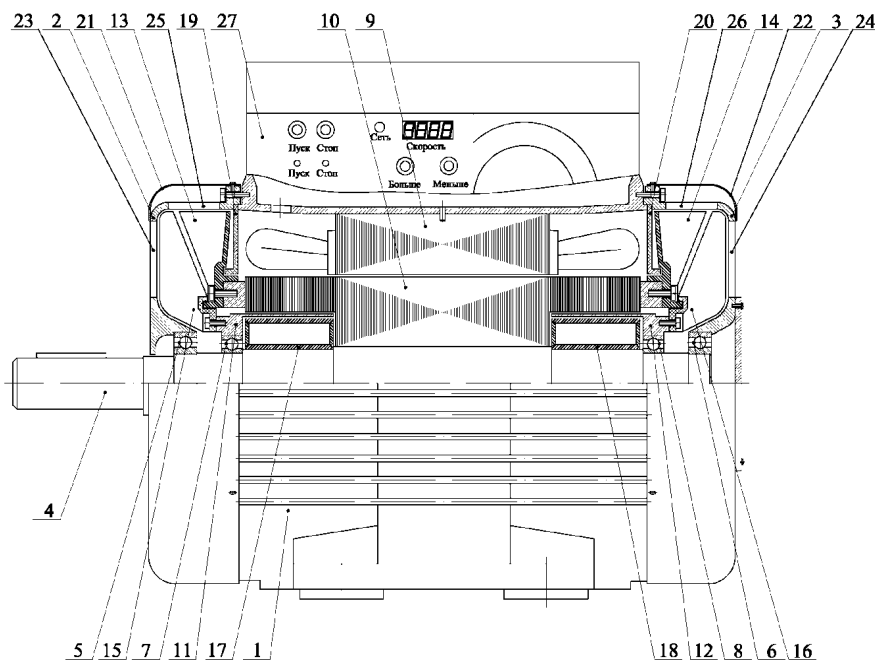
Особенности конструкции асинхронного электродвигателя по конструктивной схеме ДАС с трехроторной электромеханикой (ДАС-14): 1 – станина электродвигателя; 2, 3 – подшипниковые щиты; 4 – вал силового ротора; 5, 6 – подшипники силового ротора; 7, 8 – подшипники малых роторов вентиляторов; 9 – магнитопровод статора с обмоткой; 10 – удлиненный магнитопровод силового ротора со стержневой обмоткой; 11, 12 – малые роторы вентиляторов; 13, 14 – лопасти вентиляторов-теплорассеивателей силового ротора; 15, 16 – вентиляторы, закрепленные на малых роторах; 17, 18 – магнитопроводы малых роторов вентиляторов; 19, 20 – кольцевые перегородки; 21, 22 – кожухи; 23, 24 – радиальные отверстия подшипниковых щитов; 25, 26 – осевые отверстия подшипниковых щитов; 27 – клеммная коробка со встроенным электронным блоком регулирования
